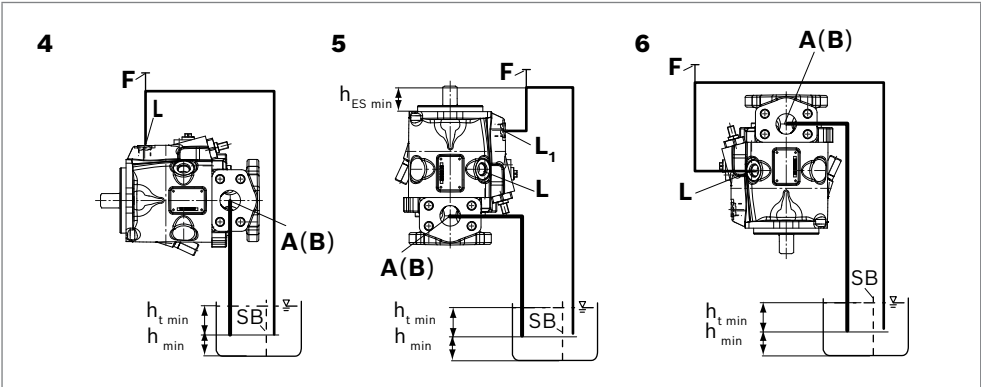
Übertankeinbau A10VZG mit Einbaulage 4–6
